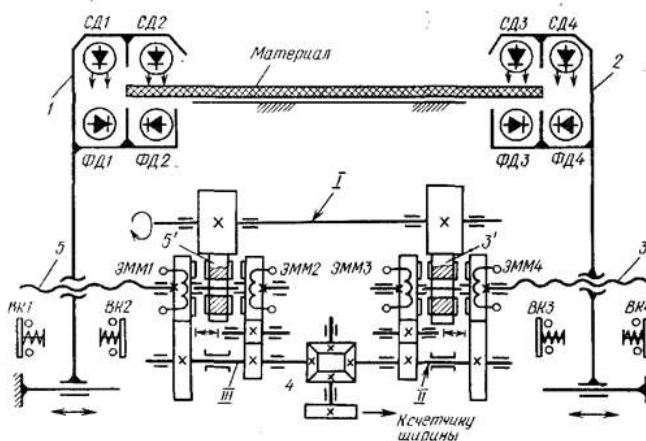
Схема автоматического устройства для измерения ширины материала на станке с подвижными фотоэлектрическими следящими головками.
